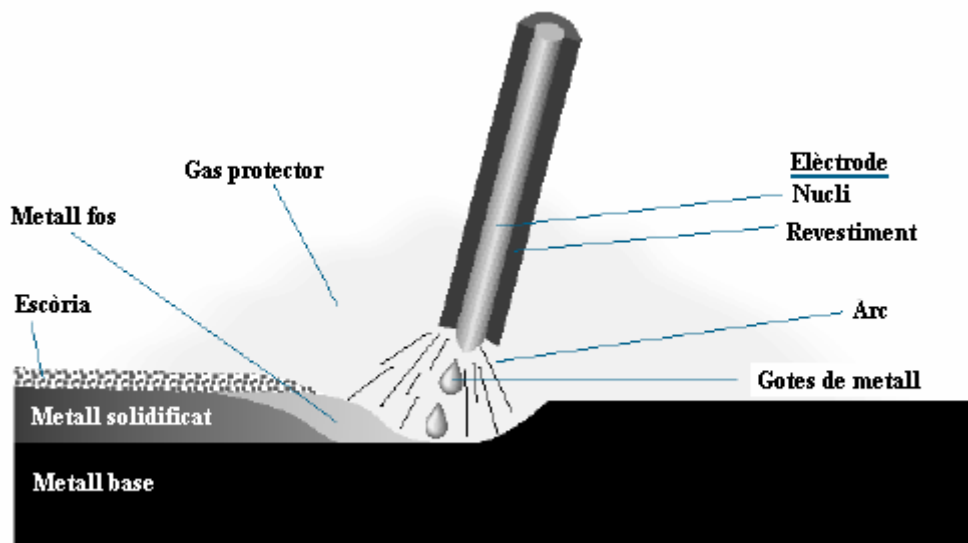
Soldadura metàl·lica amb arc protegit (SMAW)
